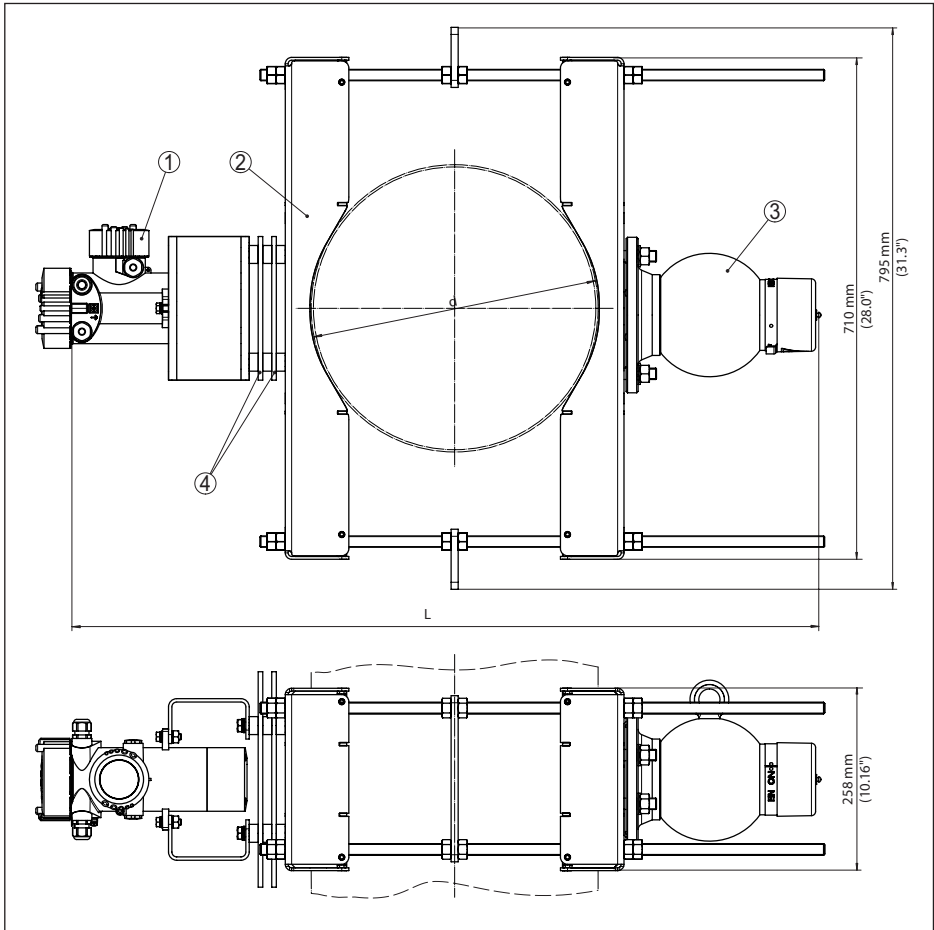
Dispositivo de apriete con sensor montado horizontalmente y kit de protección térmica
